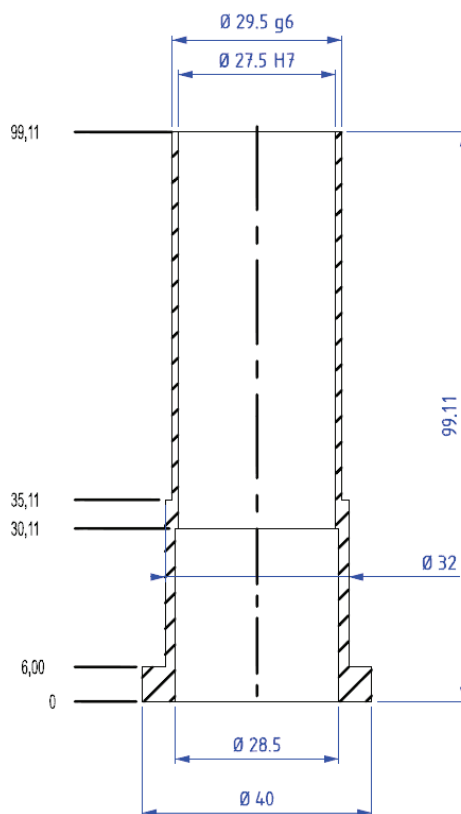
Extrator tubular (E3) - vista em corte (retirado do 2D).
